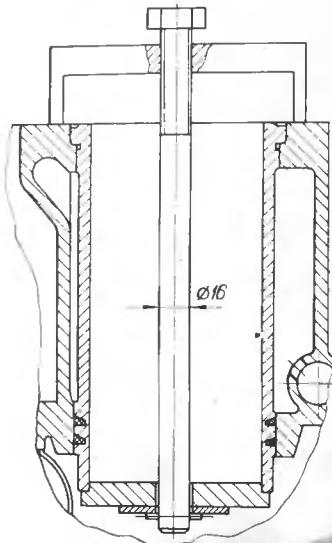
Приспособление для выпрессовки гильз цилиндров
